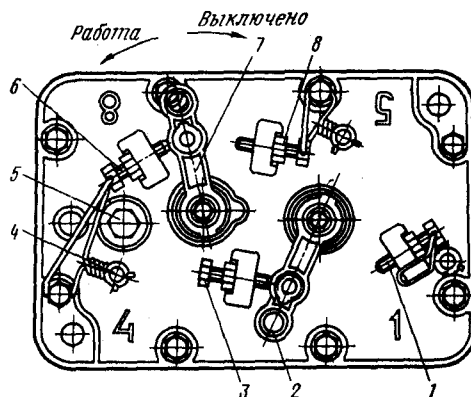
Крышка регулятора с рычагами управления регулятором и остановом двигателя
